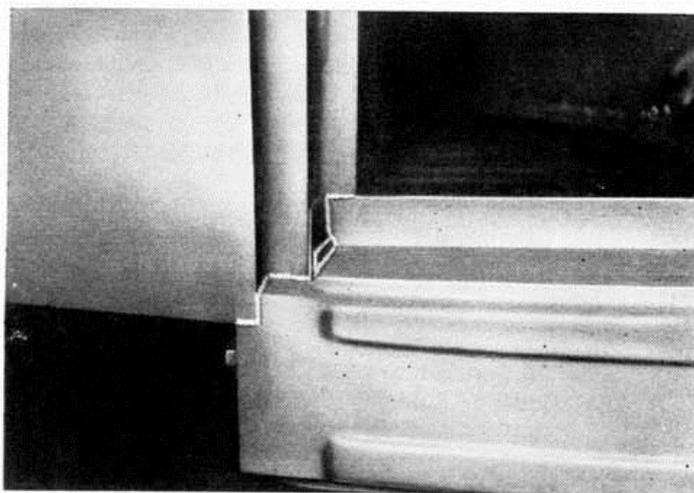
Schweißstoß im Bereich der Fahrertür
